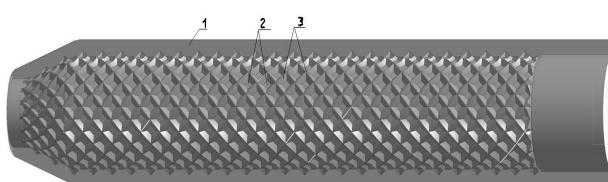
Заготовка с многозаходными спиральными нарезами встречного направления:
